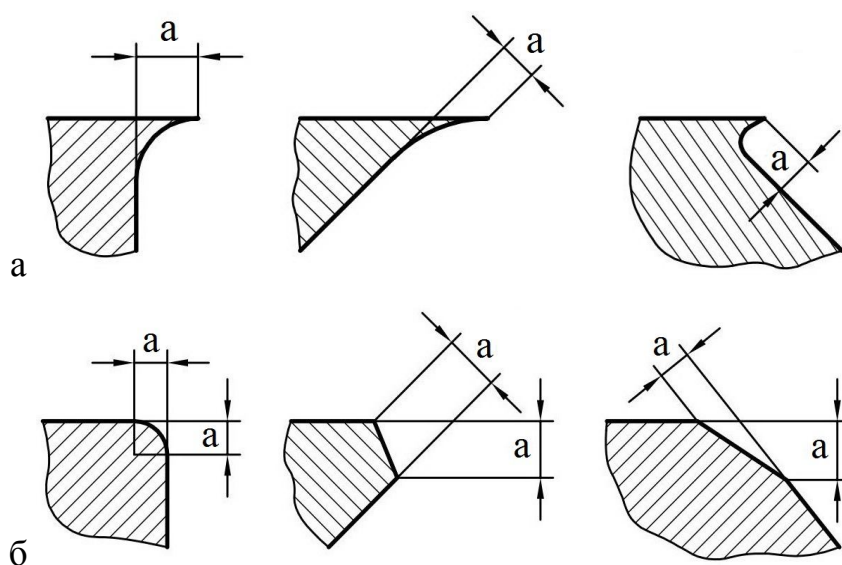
Кваліметричний показник кромки a [24]:
